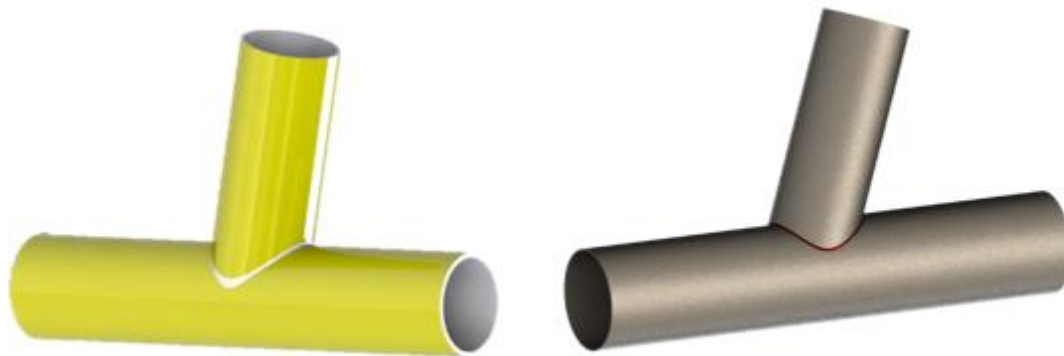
Modelos de SolidWorks de la soldadura de injertos (Fuente: Propia)
